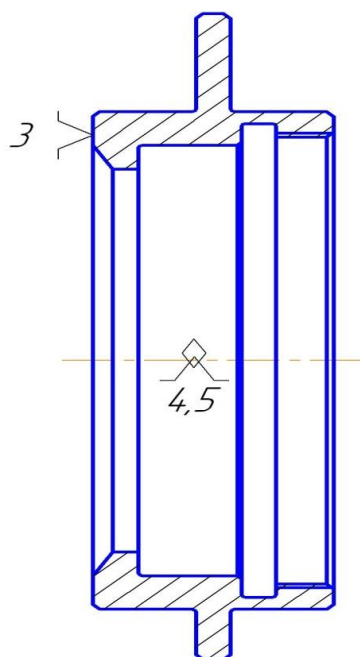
Теоретична схема базування на токарній, фрезерній, довбальній, внутрішньошліфувальній операціях
